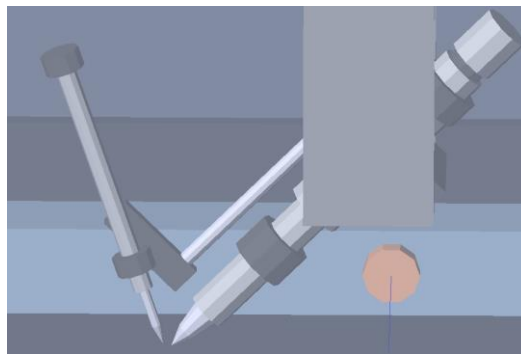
Mano Brazo Robot soldadura [10]
